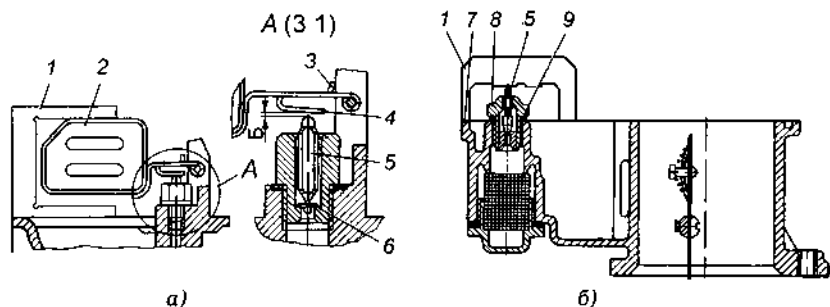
Установка поплавка и иглы клапана подачи топлива в карбюраторах: а — К-126Б; б — К-88А: 1 — калибр; 2 — поплавок; 3 — ограничитель хода поплавка; 4 — язычок; 5 — игла; 6 — шайба; 7 — корпус карбюратора; 8 — корпус клапана; 9 — прокладки; Б — зазор
